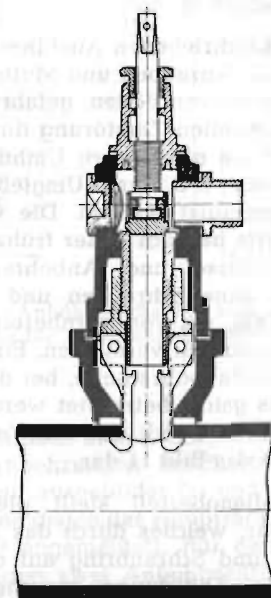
Bügelloser Anbohr-Rohranschluß für obere Anbohrung mit seitlichem Gewindeabgang
